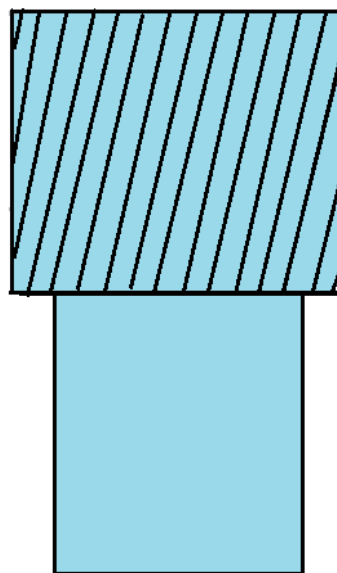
Рифленый пуансон с гладким цилиндрическим выступом
